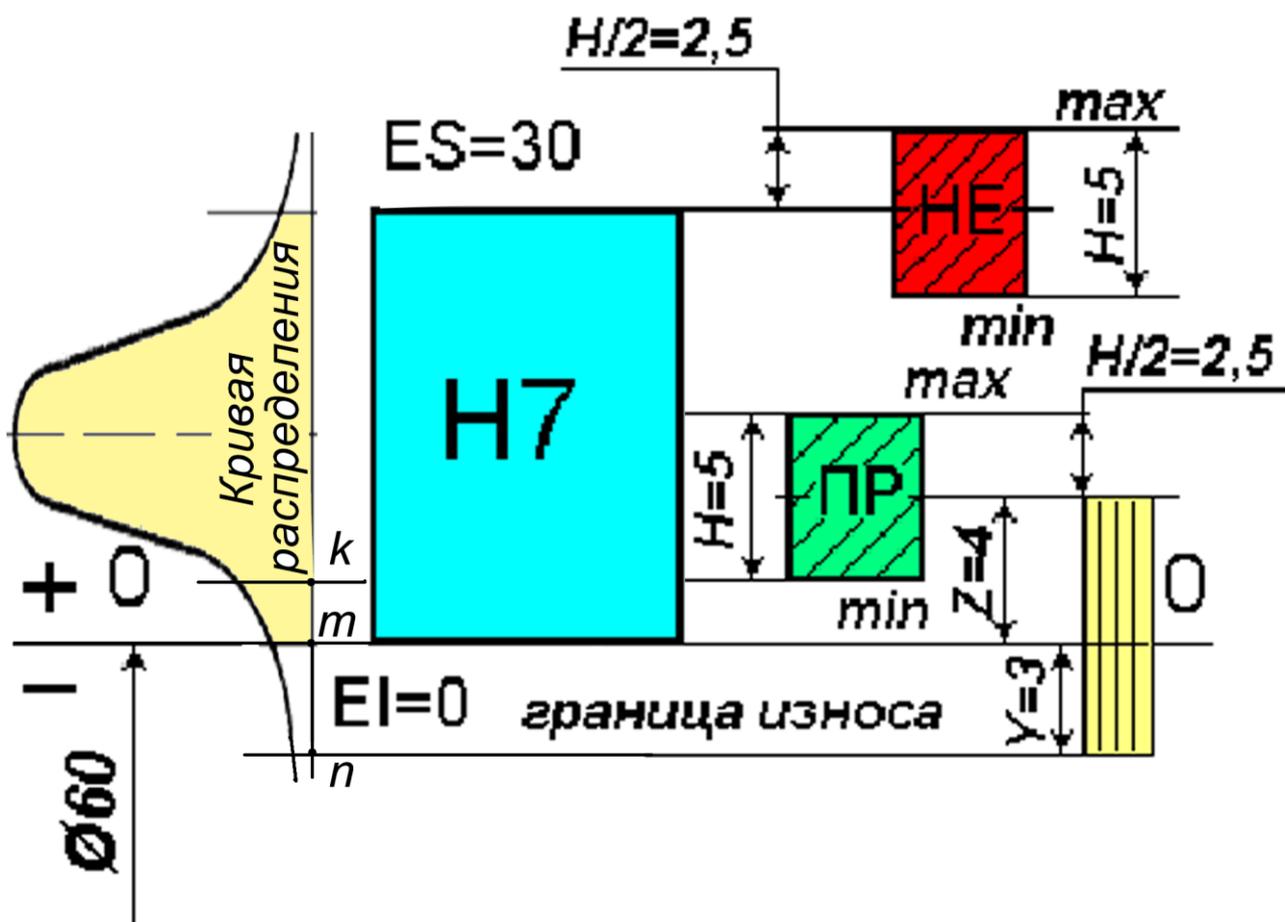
Поля допусков калибр-пробок, для поля допуска H7
